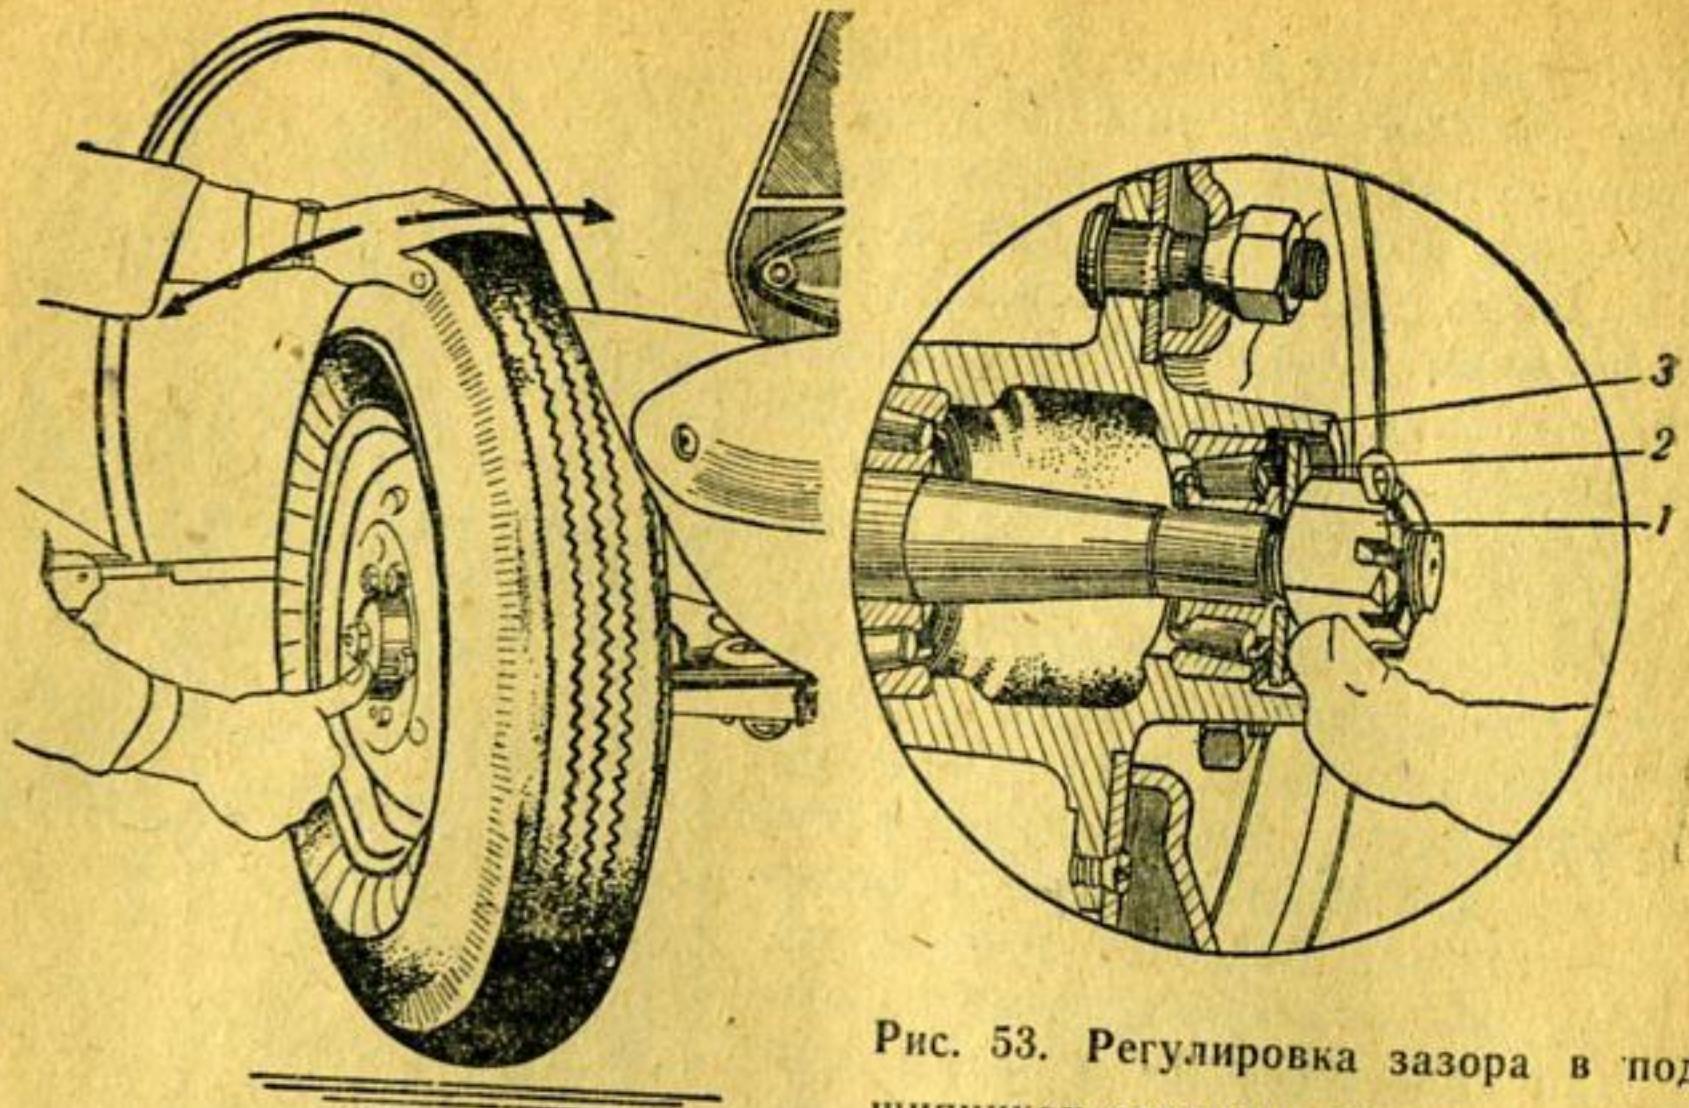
Регулировка зазора в подшипниках ступицы переднего колеса:
